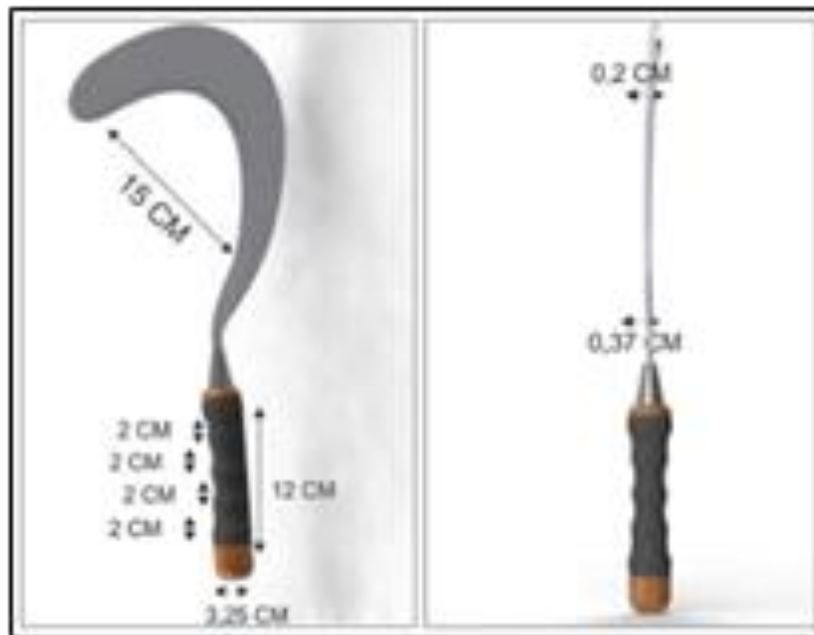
Diseño de la herramienta mejorada en SolidWorks [26].
